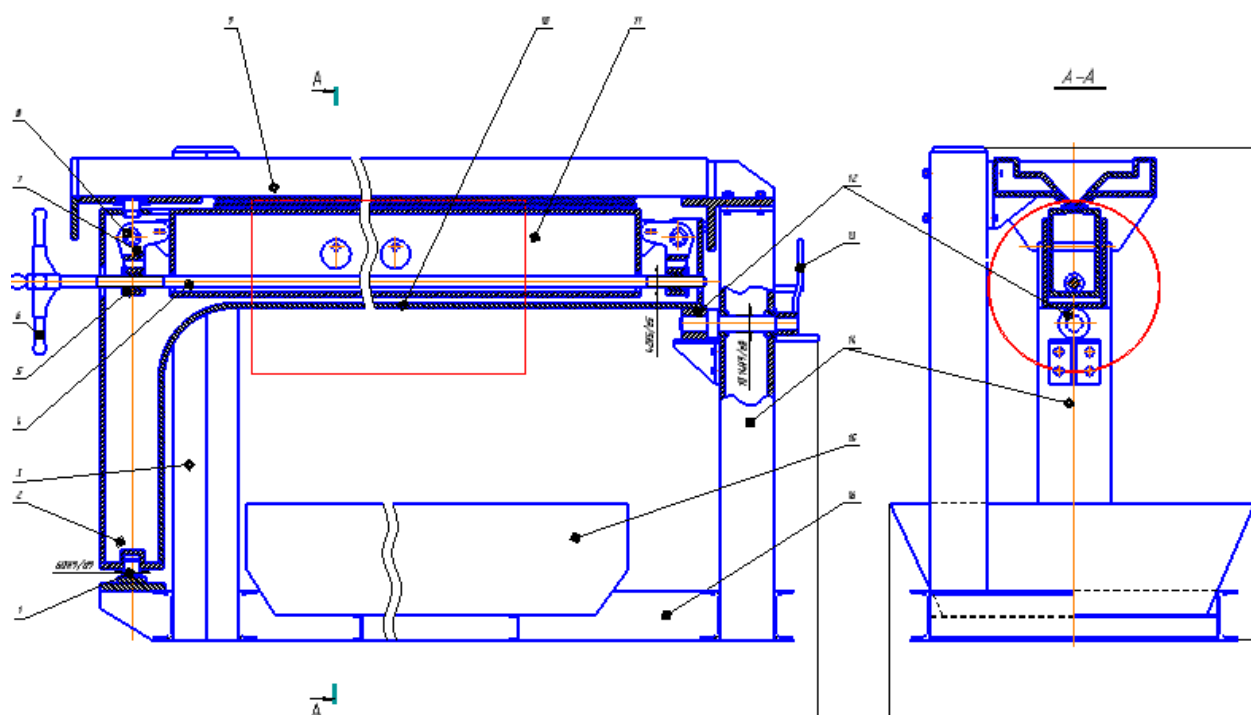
Стенд для складання і виконання поздовжнього шва обичайки балона.
